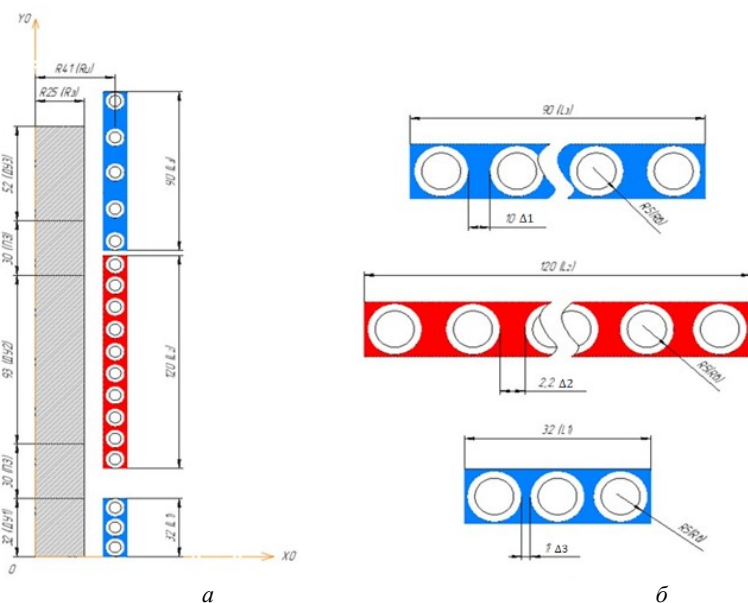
Схематичное изображение геометрической модели системы «заготовка – индуктор»:
